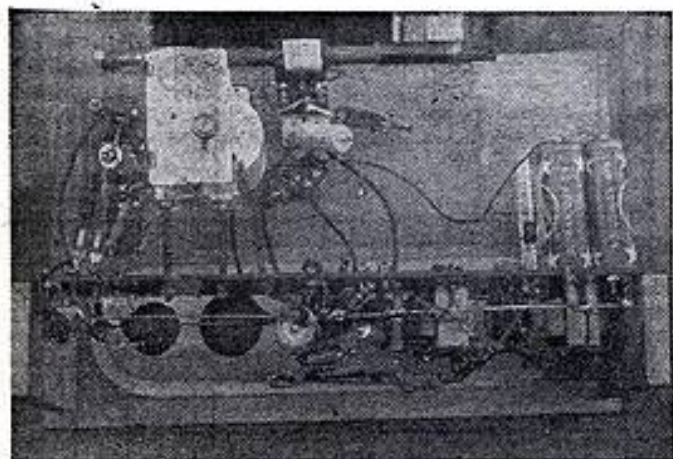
Câblage et disposition des pièces, sur le châssis. Longueur : 290 mm. — Largeur : 120 mm. — Hauteur : 54 mm.
